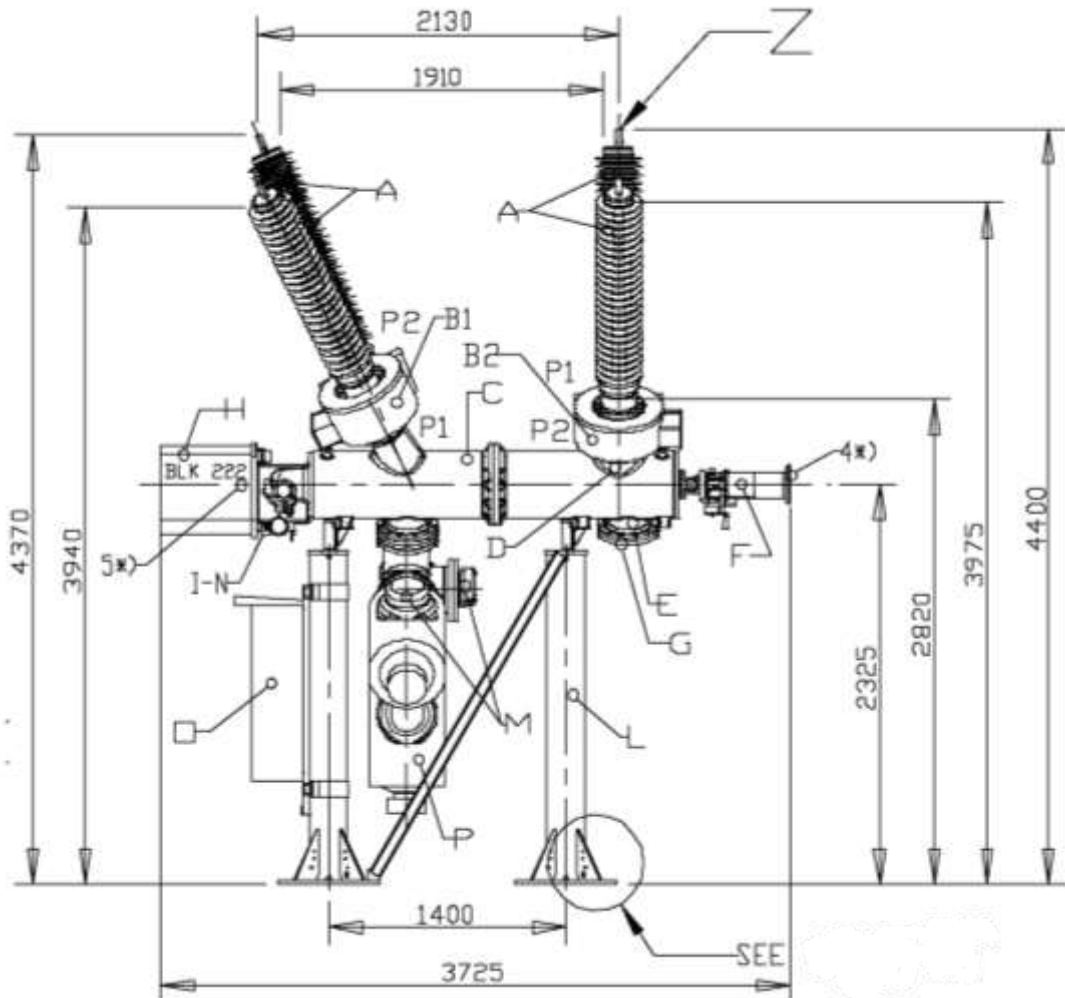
Елегазова комірка PASS MO (вигляд з боку)
